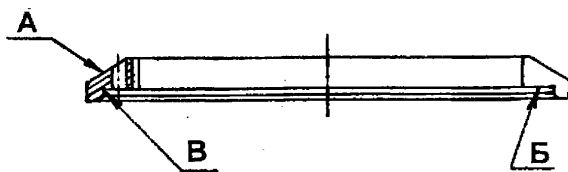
Корпус торцевого уплотнения из двух половин
